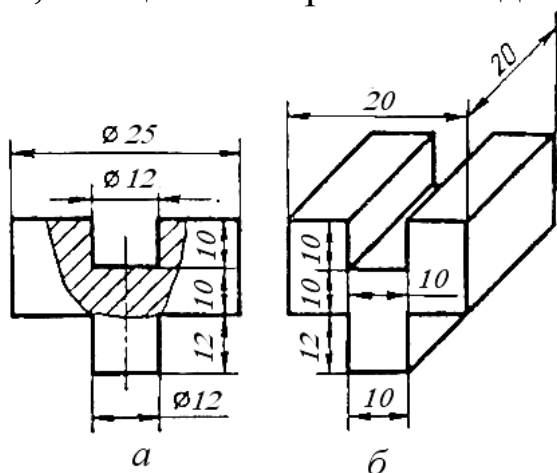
Форма и размеры образцов для испытания на чистый сдвиг (срез):
